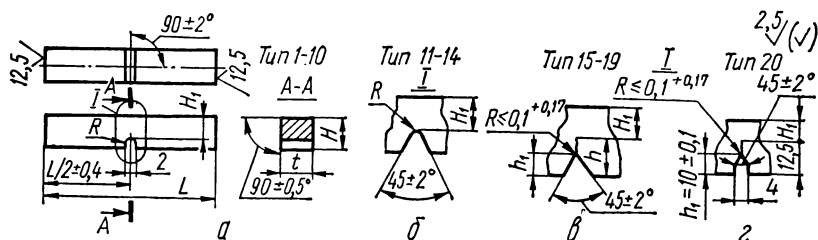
Форма и размеры концентраторов образцов на ударный изгиб [16].
